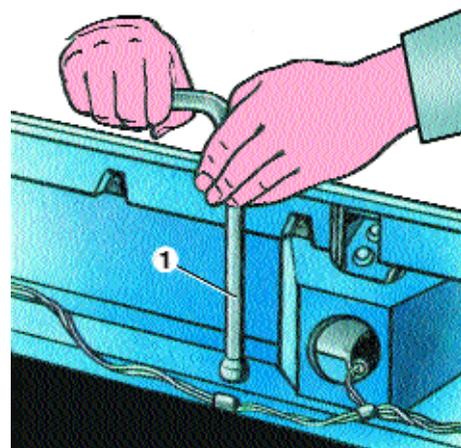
Механизм крепления запасного колеса: 1 – замок держателя запасного колеса; 2 – держатель запасного колеса
